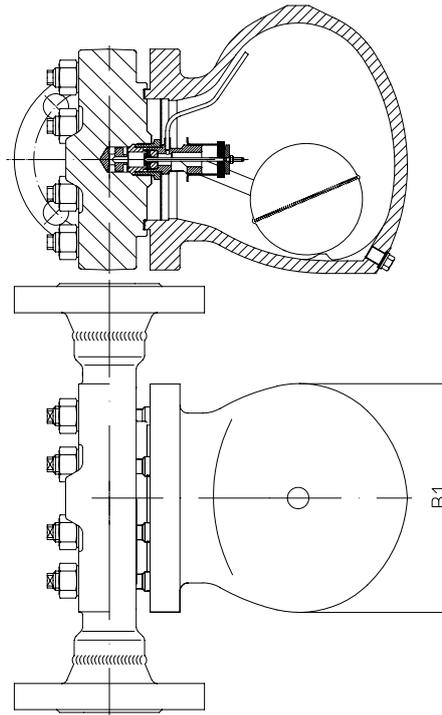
1 mit Flanschen - horizontale Einbaulage
